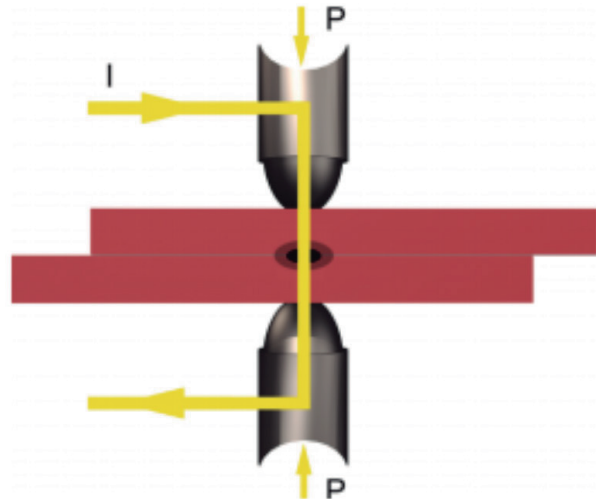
Esquema del proceso de soldadura por resistencia. [5]
